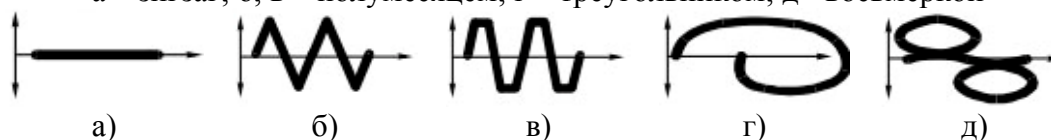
Траектории перемещения сварочной горелки при роботизированной сварке: а – без осцилляций; б – зигзаг; в – трапеция; г – спираль; д – восьмёрка
